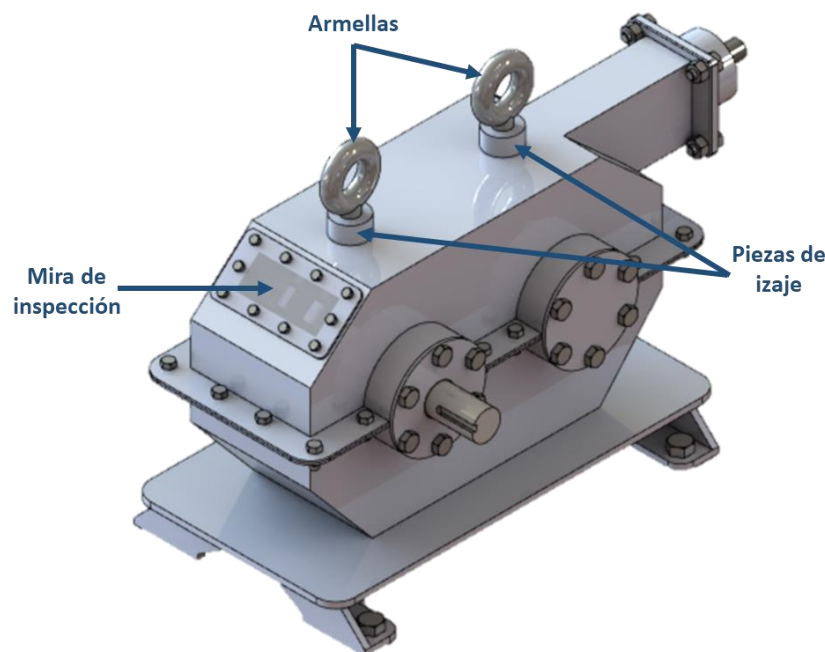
Mira de inspección y zonas de izaje del reductor.
